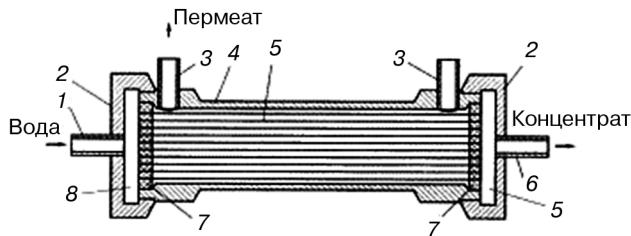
Аппарат с полыми волокнами: 1 — патрубок для подачи исходной воды; 2 — крышки; 3 — патрубок пермеата; 4 — корпус; 5 — полые волокна; 6 — патрубок для отвода концентратата; 7 — герметизирующая заливка; 8 — концевые камеры
